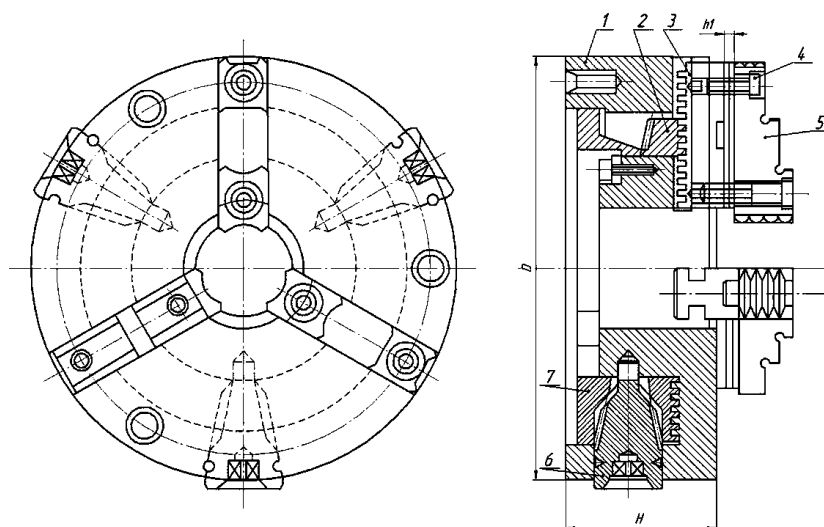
Трьохкулачковий самоцентруючий патрон
